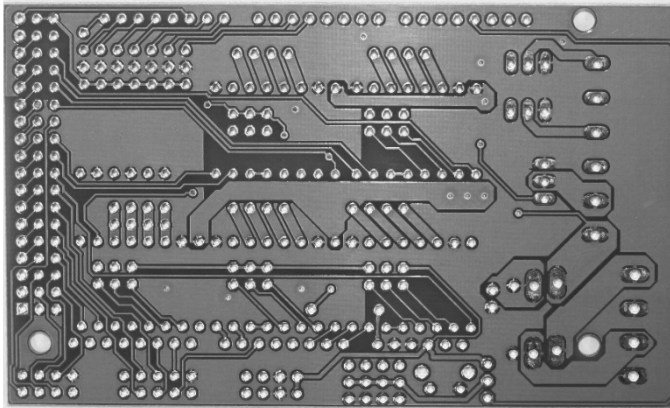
PCB integrada por un conjunto de pistas y puntos de aterrizaje
